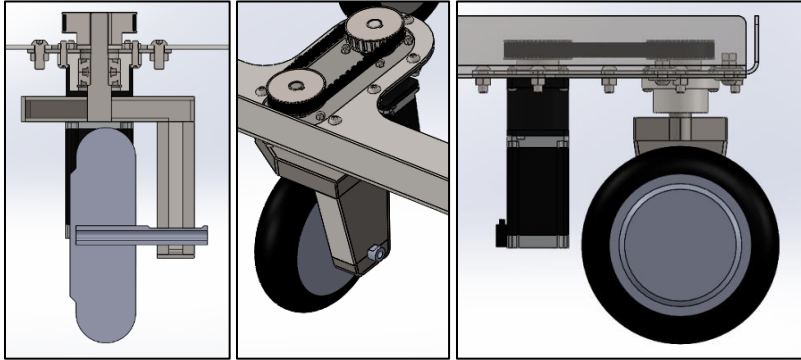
Ensamblaje final acoplamiento módulo de dirección y tracción.
